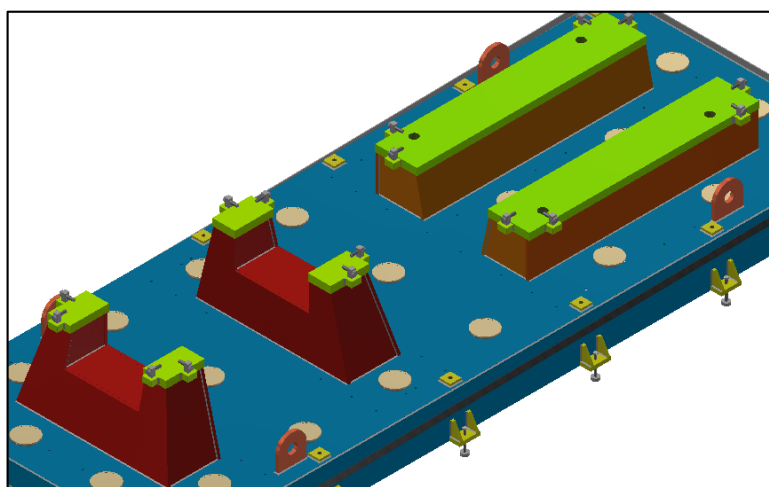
7 Pedestales unidos mediante soldadura a la chapa metálica
